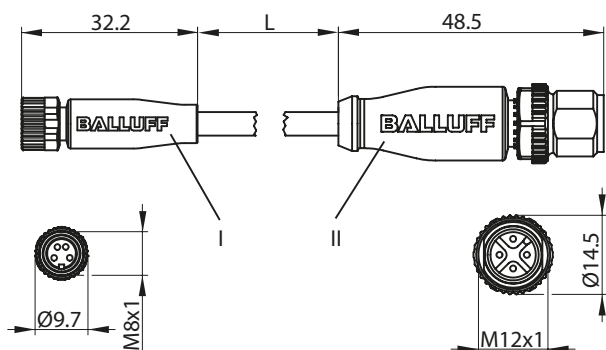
Connecteur femelle droit – connecteur mâle droit
